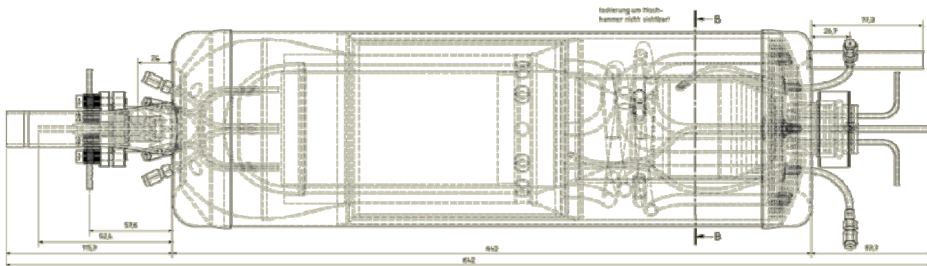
Entwurfszeichnung des ATR AH3 nach Abstimmung mit dem Presswerk Struthütten. Ausschnitt Seitenansicht mit Einblick auf die Verrohrung der Luftzuführung.
